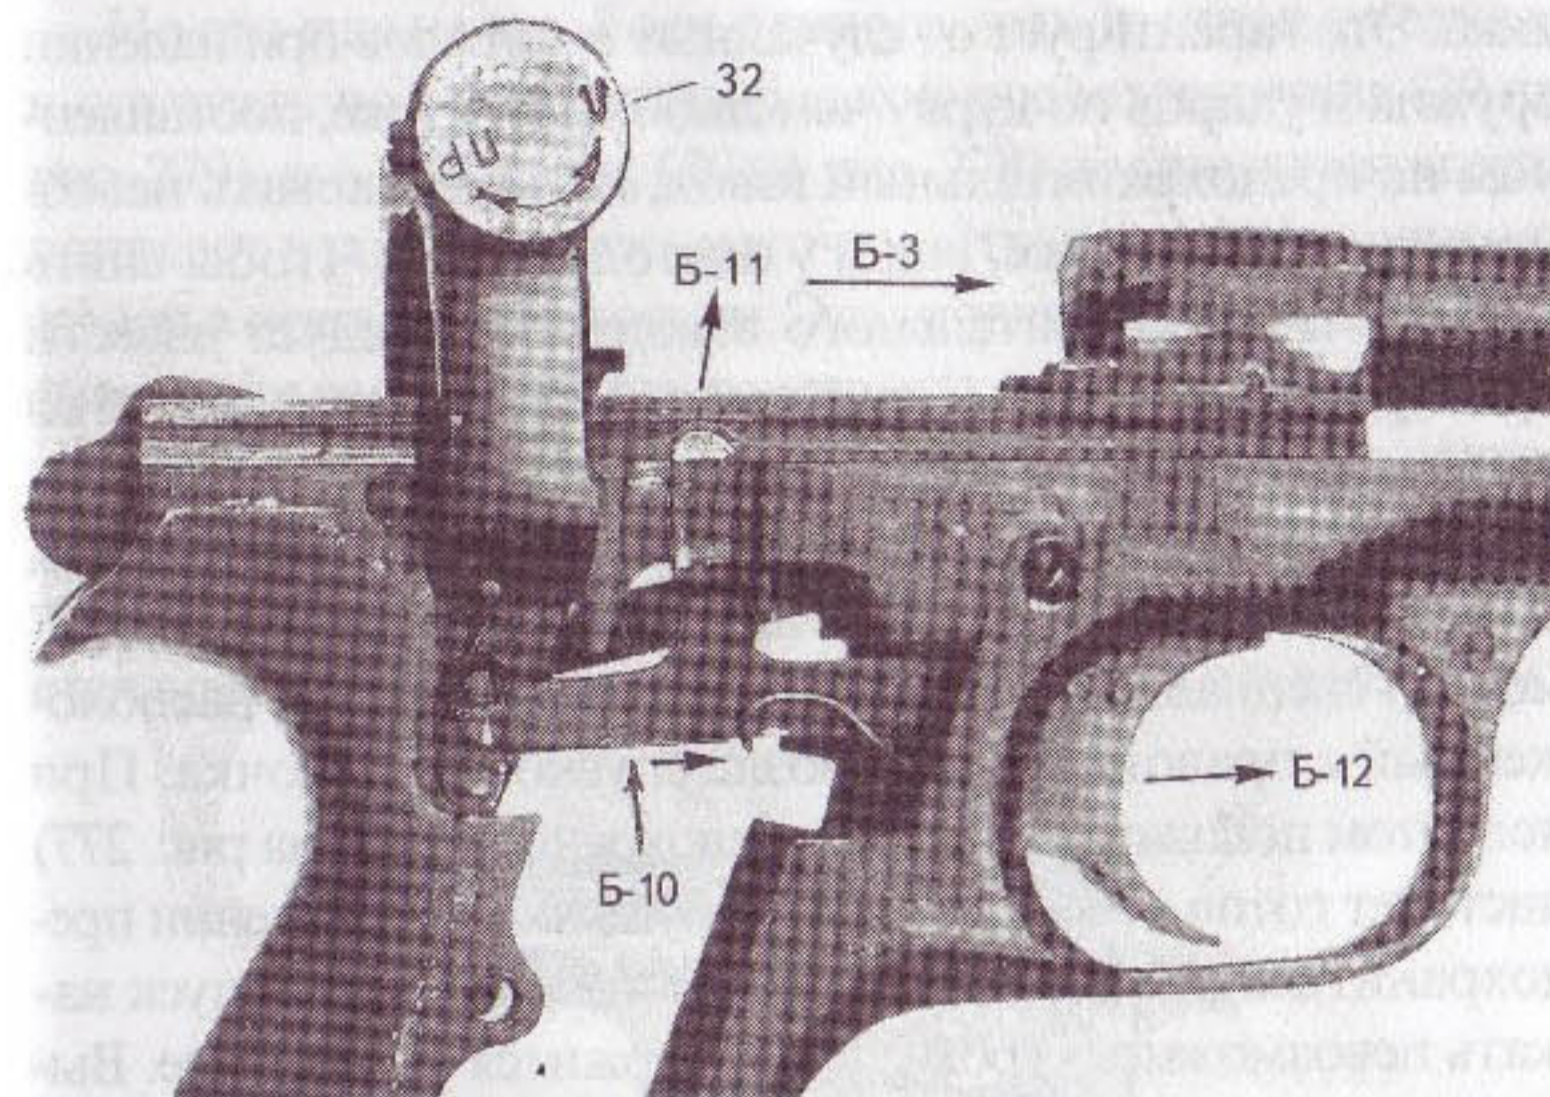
Положение курка и разобшающего механизма перед следующим выстрелом
